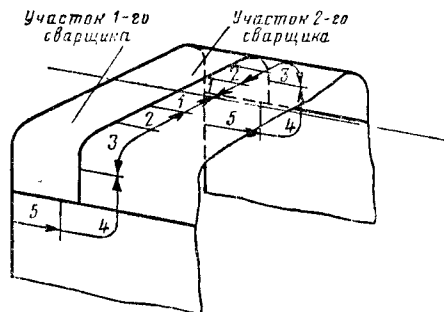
Порядок приварки полустенки к огневой коробке паровозной топки
